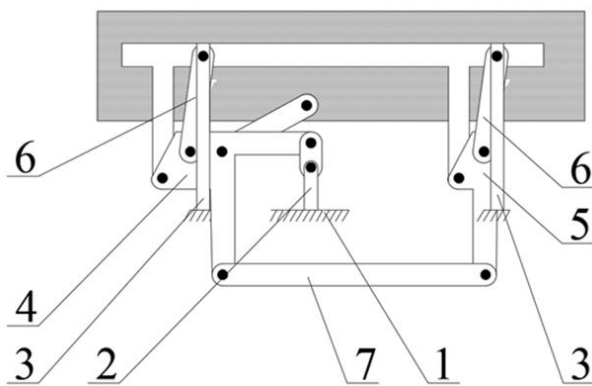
Інерційний конвеєр для транспортування сипких матеріалів: 1 – нерухома основа; 2 – електродвигун з кривошипним механізмом; 3 – стойка; 4 – головне коромисло; 5 – вторинне коромисло; 6 – важіль приводу зворотно-поступового руху жолобу; 7 – з'єднувальна тяга.
